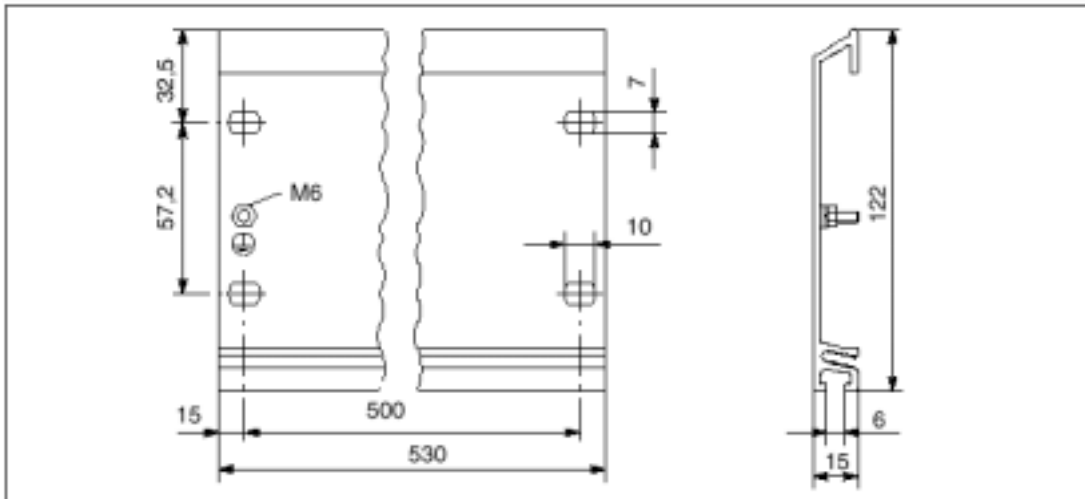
Чертеж с размерами профильной шины стандартной ширины 530 мм
